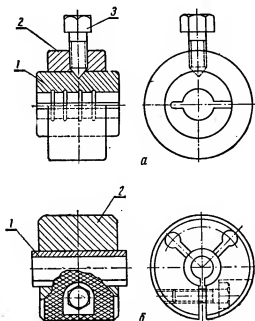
Притиры для черновой (а) и чистовой (б) притирки наружной цилиндрической поверхности:
